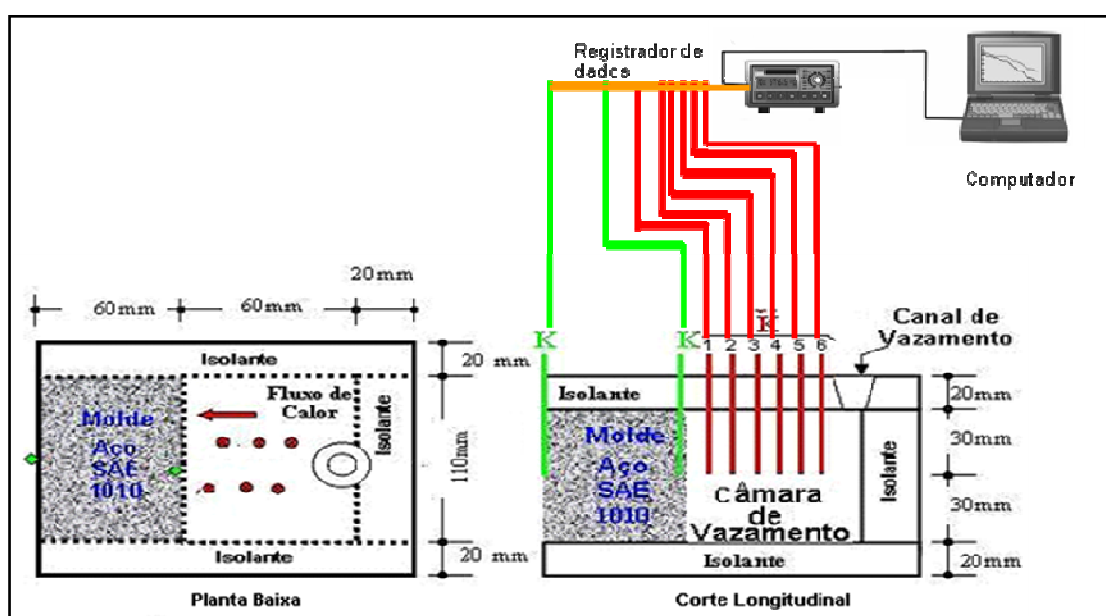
Esquema ilustrativo do sistema metal/molde: planta baixa e corte longitudinal da câmara de vazamento.
